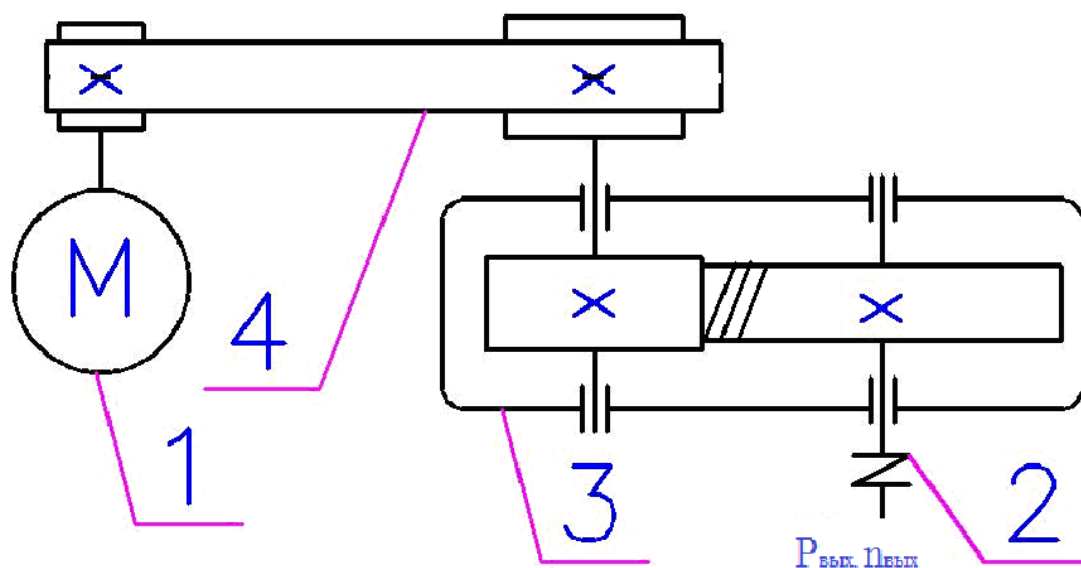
Кинематическая схема привода рычажного механизма
